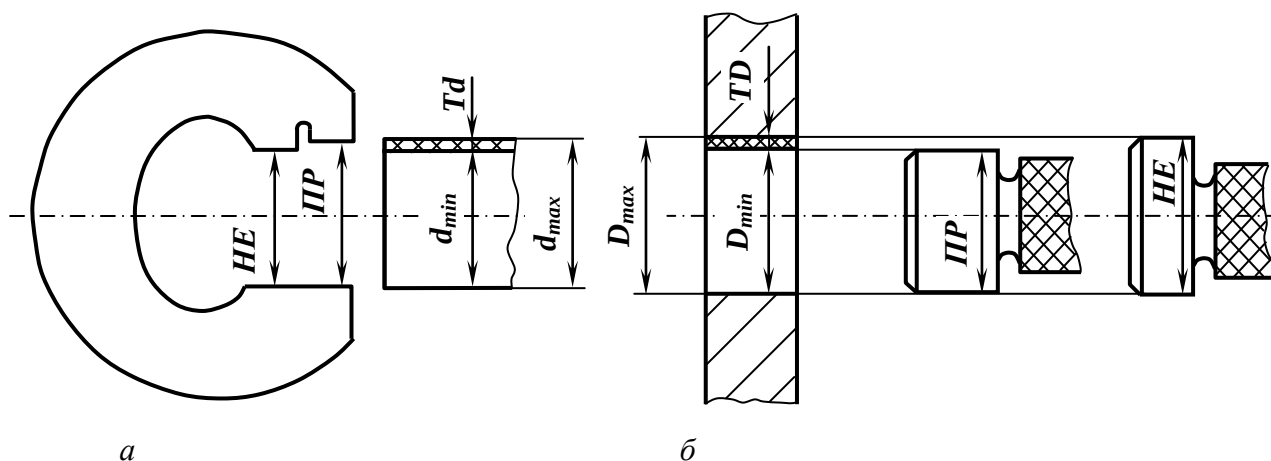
Схемы контроля деталей: *а*– вала скобой; *б*– отверстия пробками
